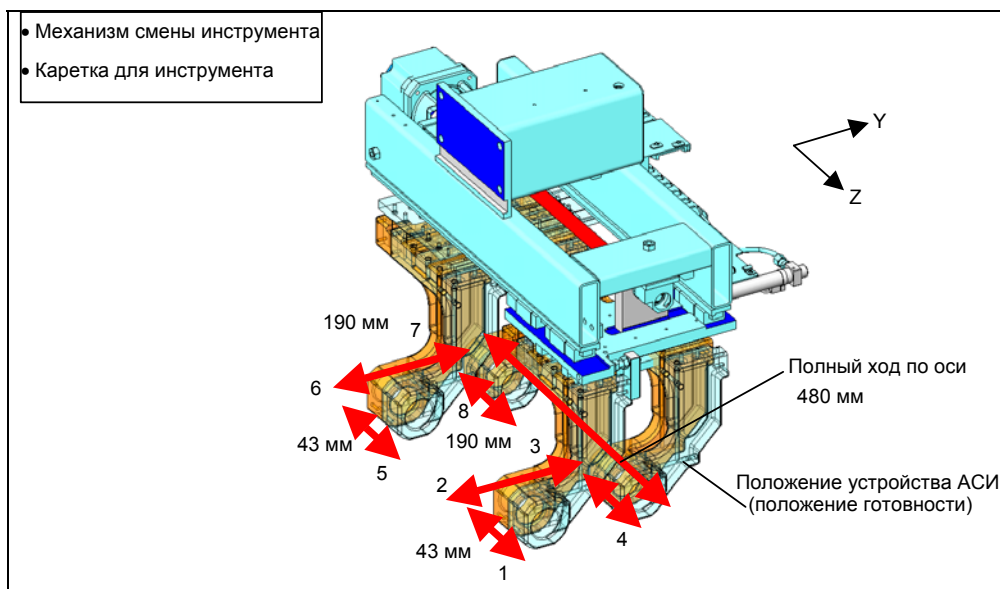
Перемещения механизма смены инструмента и каретки для инструмента (для станка с магазином на 72 инструмента)
